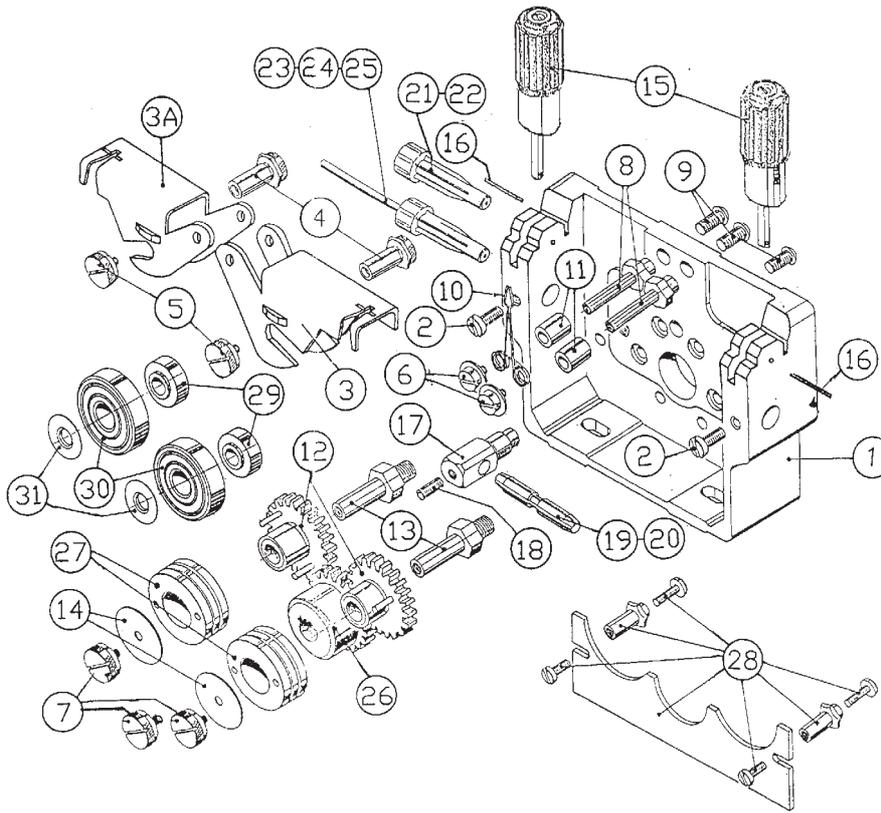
/7a Explosionszeichnung Drahtvorschubeinheit 4-Rollenantrieb /
